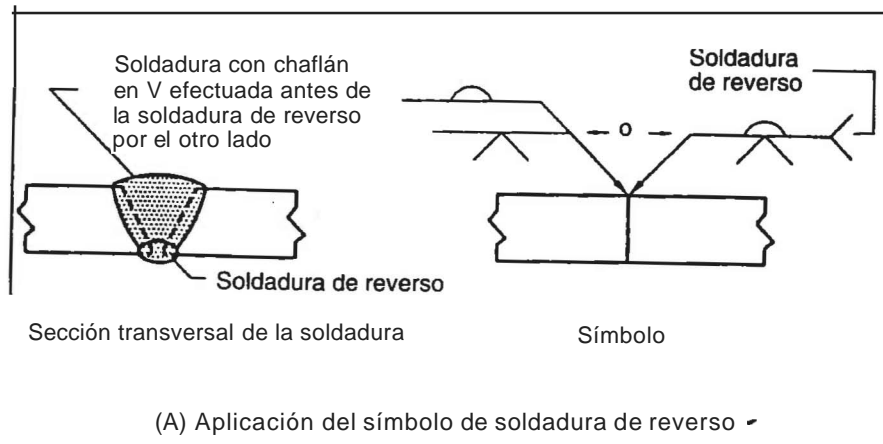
APLICACIONES DEL SÍMBOLO DE SOLDADURA DE REVERSO O RESPALDO
